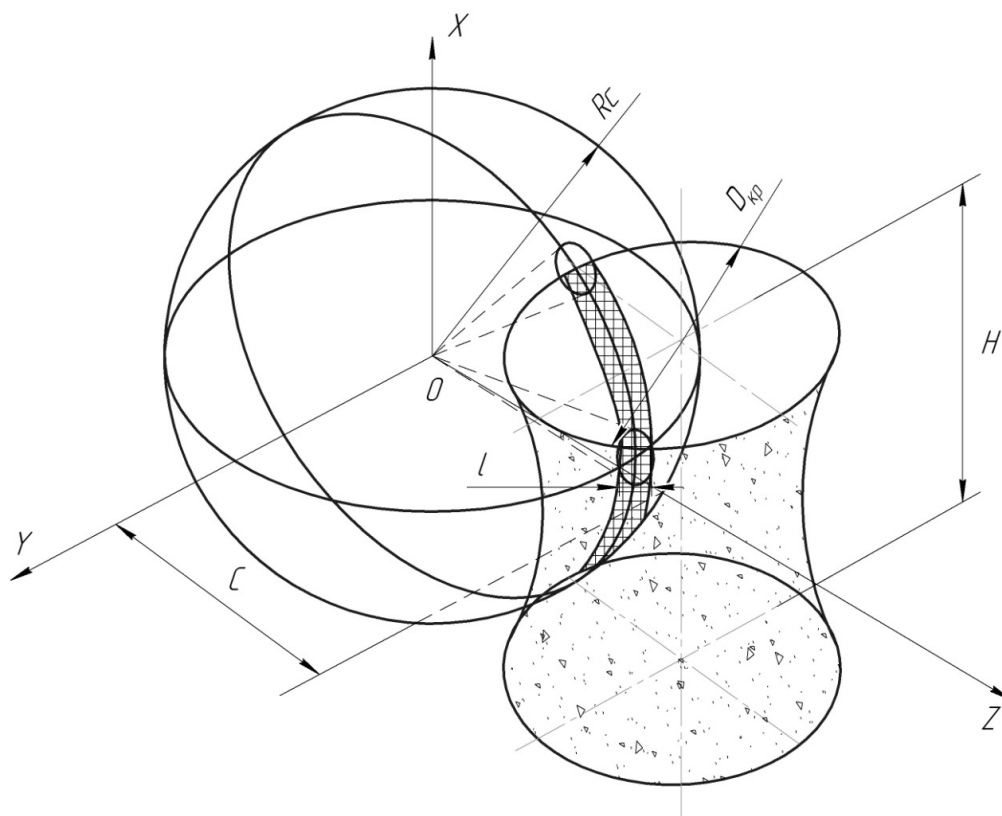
Схема определения длины контакта детали с инструментом при непрерывном шлифовании периферией шлифовального круга
